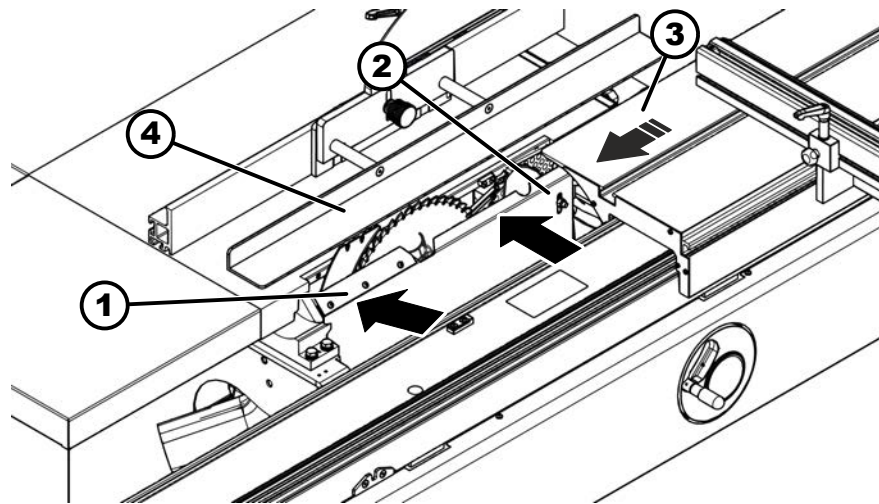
Betriebsbereitschaft - Nutwerkzeuge
